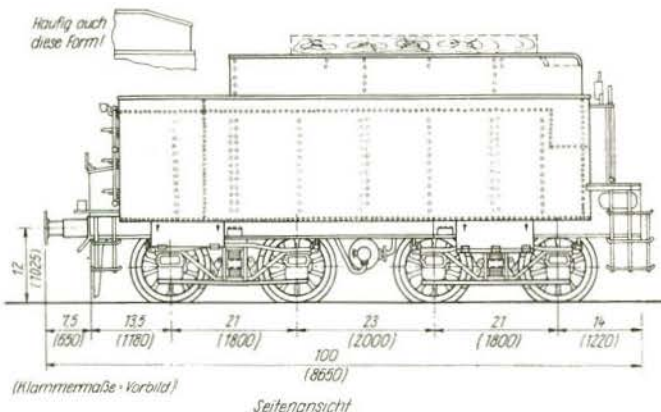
Die Seitenansicht des Tenders. Die beiden Seiten des Kohlekastenaufbaues sind häufig auch vorn nach unten abgechrägt (siehe Zeichnung oben links).
